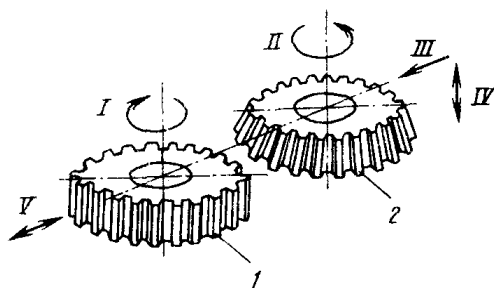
Схема зубодолбления цилиндрических зубчатых колес: I – движение заготовки зубчатого колеса; II – движение долбяка; III – движение подачи врезания; IV – возвратно-поступательное движение долбяка; V – движение отвода заготовки; 1 – заготовка, 2 – долбляк
